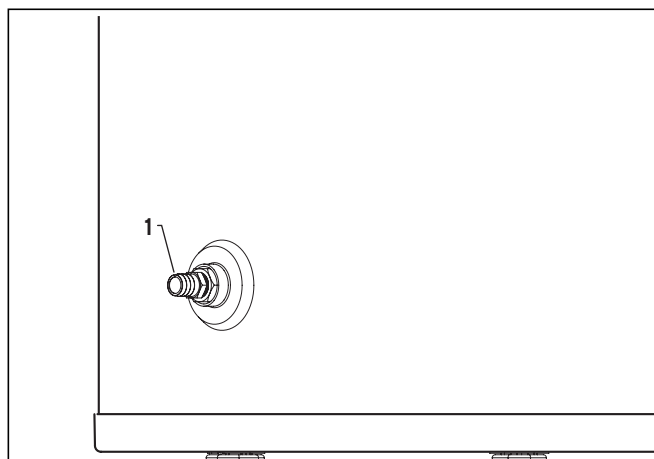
Вентиль опорожнения накопителя холодной водопроводной воды
